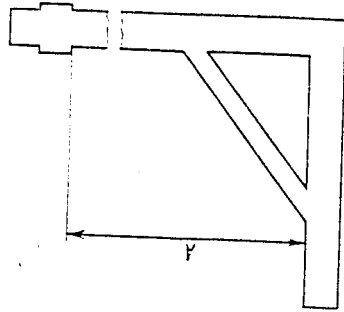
Приспособление для контроля вылета лобовых частей
